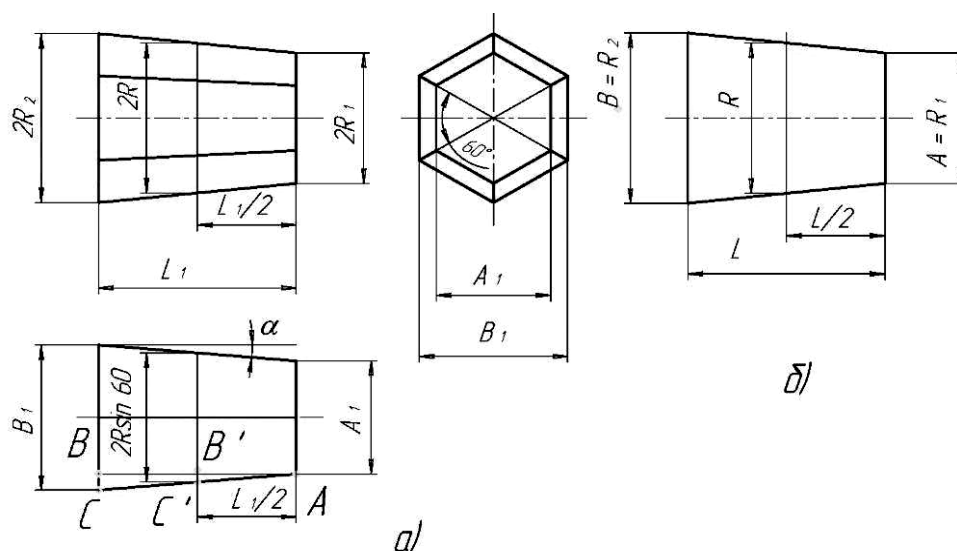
Облаштування пірамідального барабана: а – схема; б – будова грані барабана
